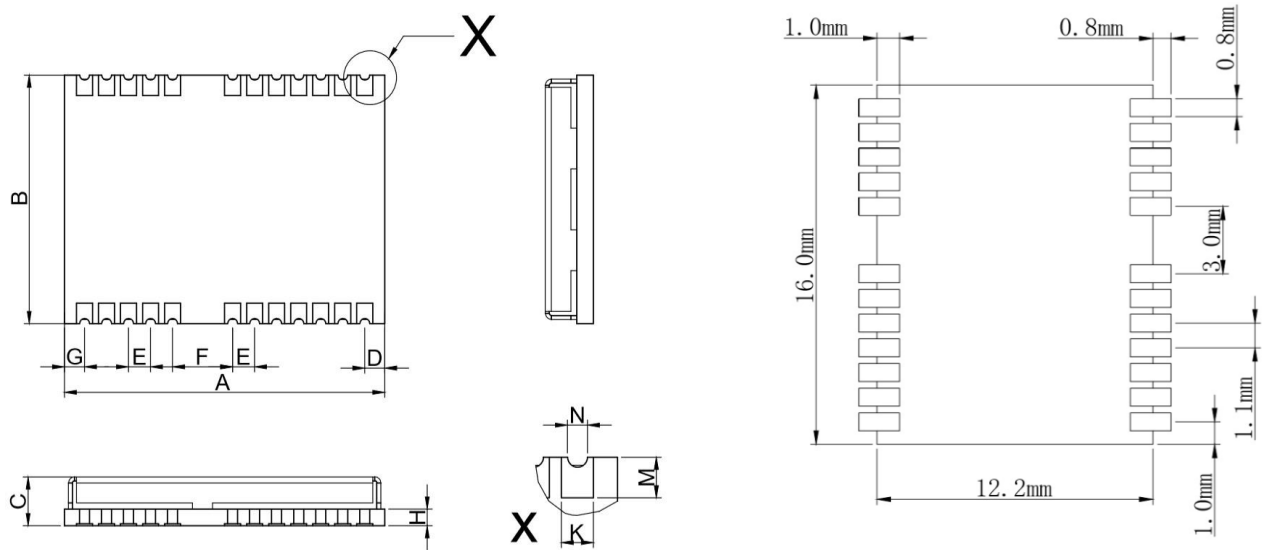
MXT909U 外形尺寸及 PCB 封装参考
